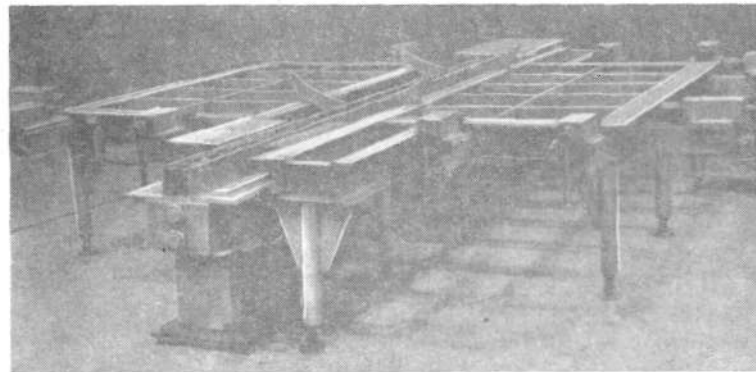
Постель с флюсовой подушкой и прижимами для сборки и сварки плоских конструкций и продольных стыков обечаек.
